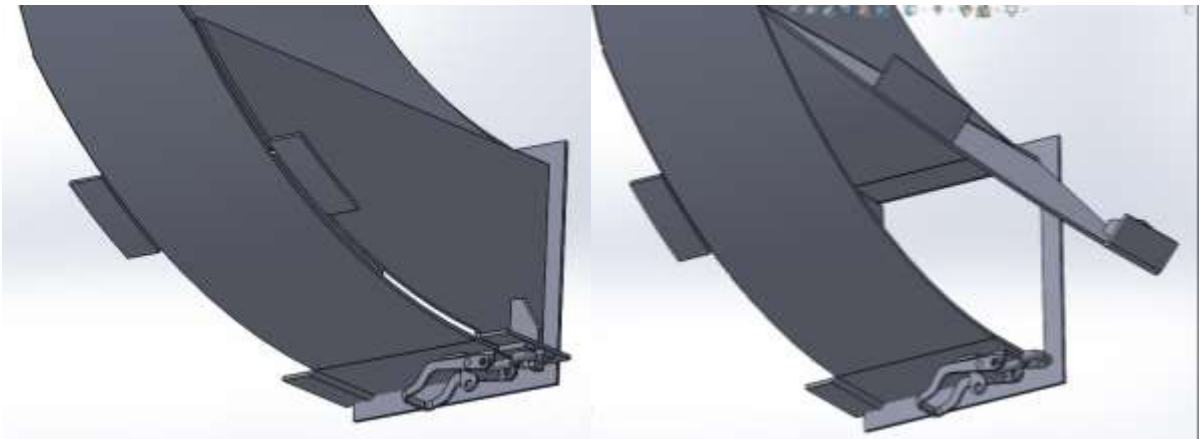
Esquema de tapa de inspección. A la izquierda, conjunto cerrado. A la derecha: posición representativa del movimiento de la tapa de inspección.
